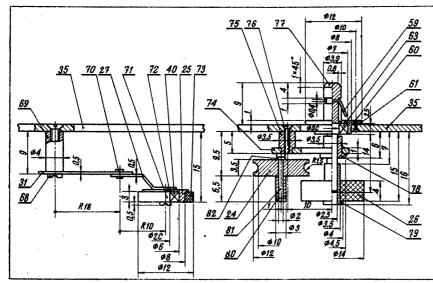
Приемный узел: 24 — шкив, эбонит, напрессовать на дет. 79; 27, 31 — рычаг, Л62-Т; 35 — шасси ЛПМ; 40 — подшинник шариковый Ашариковый 1000092 (6×2×2,3 мм); 59 — фиксатор, проволока стальная класса ІІ диаметром 0,4 мм, запрессовать в дет. 77; 60 — заклепка Ø 1 мм, 2 шт.; 61 — втулка, Ст. 45; 63 — подшипник шариковый 2000083 (7×3×2.5); 68— винт M2×4; 69— стойка, Л62-Т; 70 заклепка Ø 2 мм, Ст. 20; 71 — ось, Ст. 45; 72 — шайба, текстолит толщиной 0,5 мм; 73— кольцо, резина НО-68-1, приклеить к дет. 25 клеем 88-н; 74 — планка, Л62-Т; 75 — стойка, Ст. 20; 76 — винт М2×5; 77 — валик, Ст. 2X13; 79 — втулка, Л62-Т; 80 гайка M2; 81 — ось, Ст. 2X13; 82 шайба, текстолит толщиной 0,5 мм.
